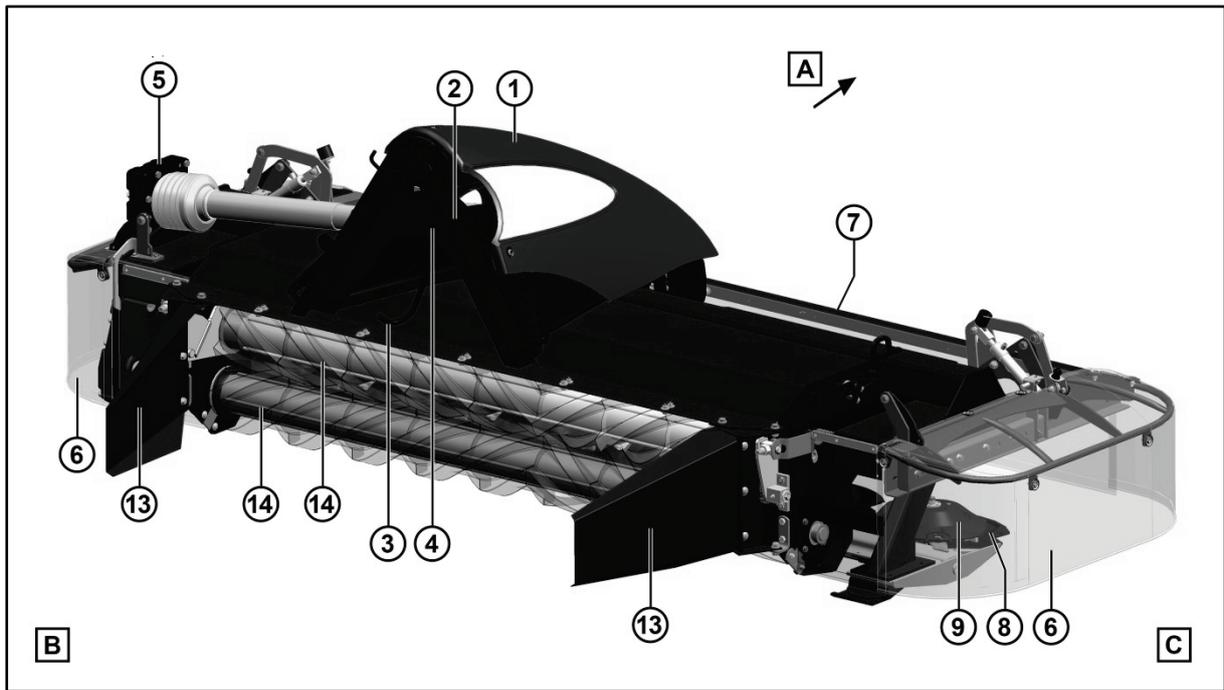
Componentes de la máquina SM 3060 FP-RC
